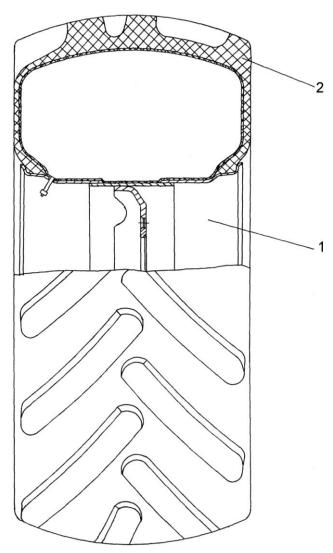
Колесо КЗК 0118000-02 и КЗК 0118000-03
